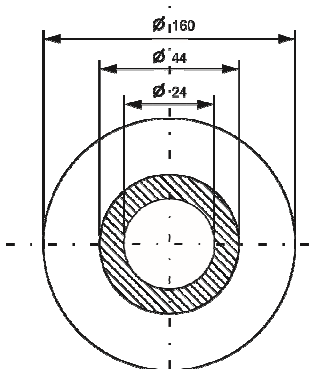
3 - Seção do queimador, com as dimensões em milímetros.
